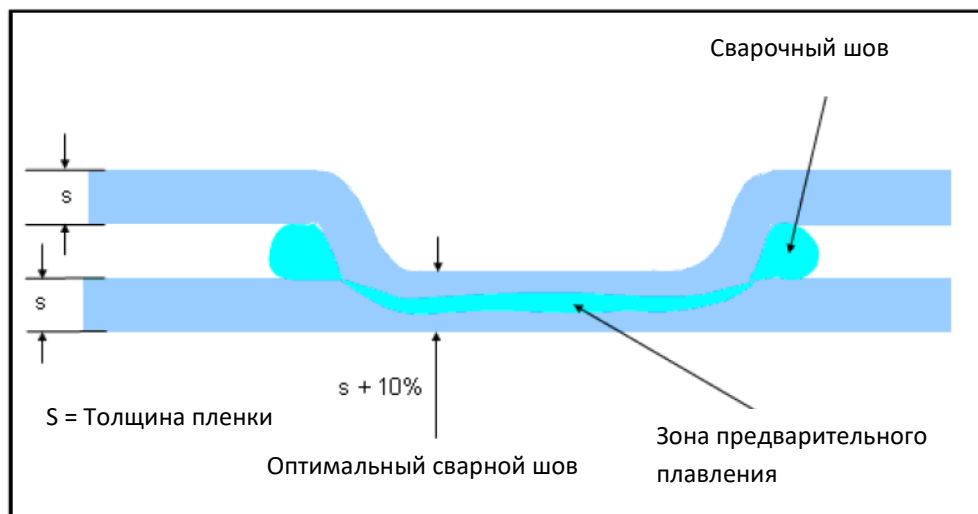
Схематическое изображение сварного соединения.
